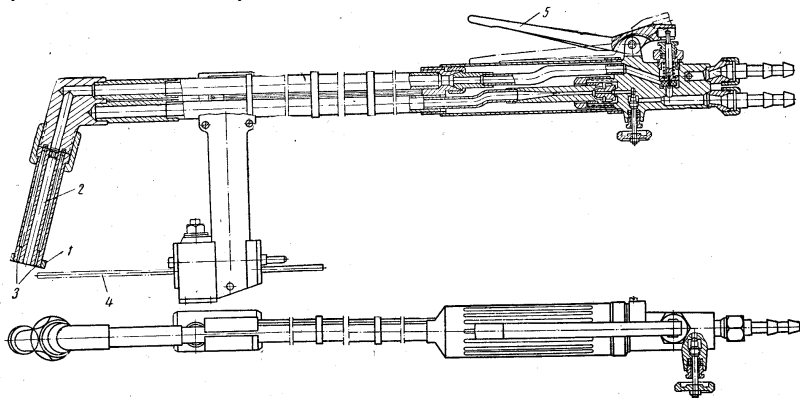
Резак для поверхностной резки и выплавки пороков
